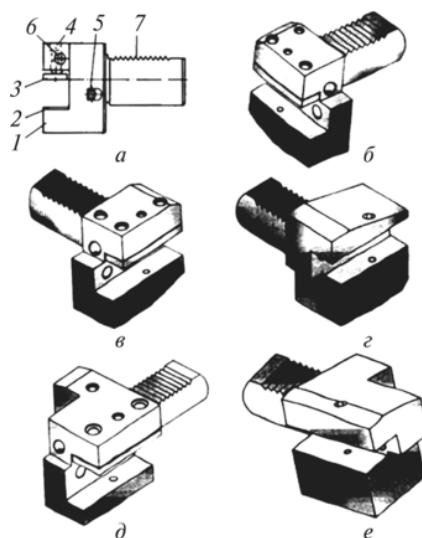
Схема (а) и общие виды (б–е) резцедержателей с цилиндрическими хвостовиками для токарных станков с ЧПУ с револьверными головками
